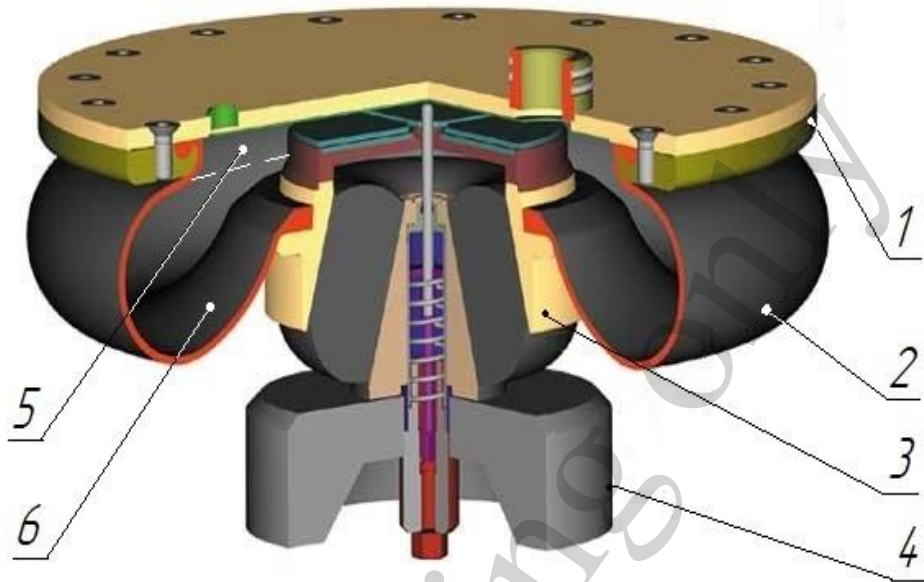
Пневморесора «діафрагмового» типу: 1 – верхнє днище; 2 – гнучка оболонка; 3 – пружний буфер; 4 – опорна плита; 5, 6 – «активна» та «пасивна» частини ємності пневморесори – відповідно
